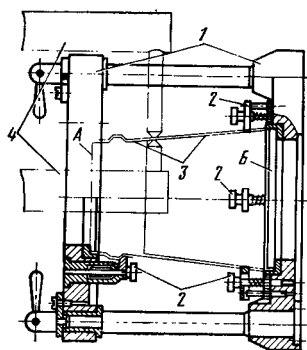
Приспособление для сварки изделий на точечной сварочной машине:
